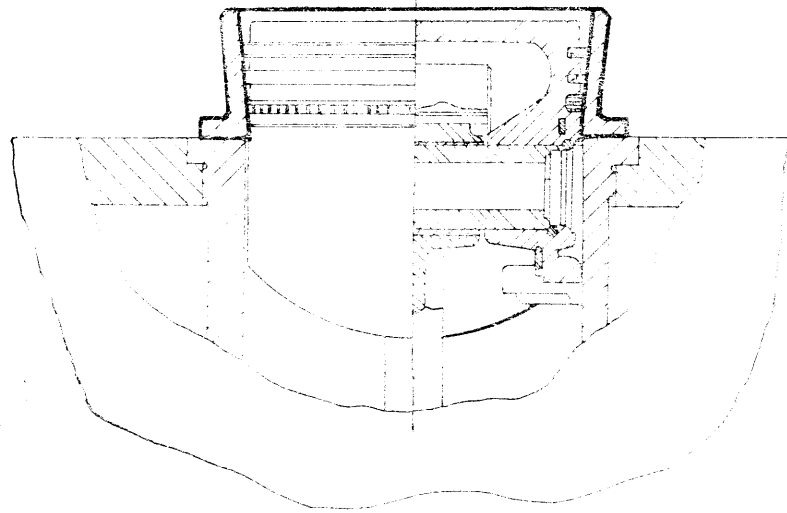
Einbau der Baugruppe Kolben und Pleuelstange mittels des Montageringes M 23.
